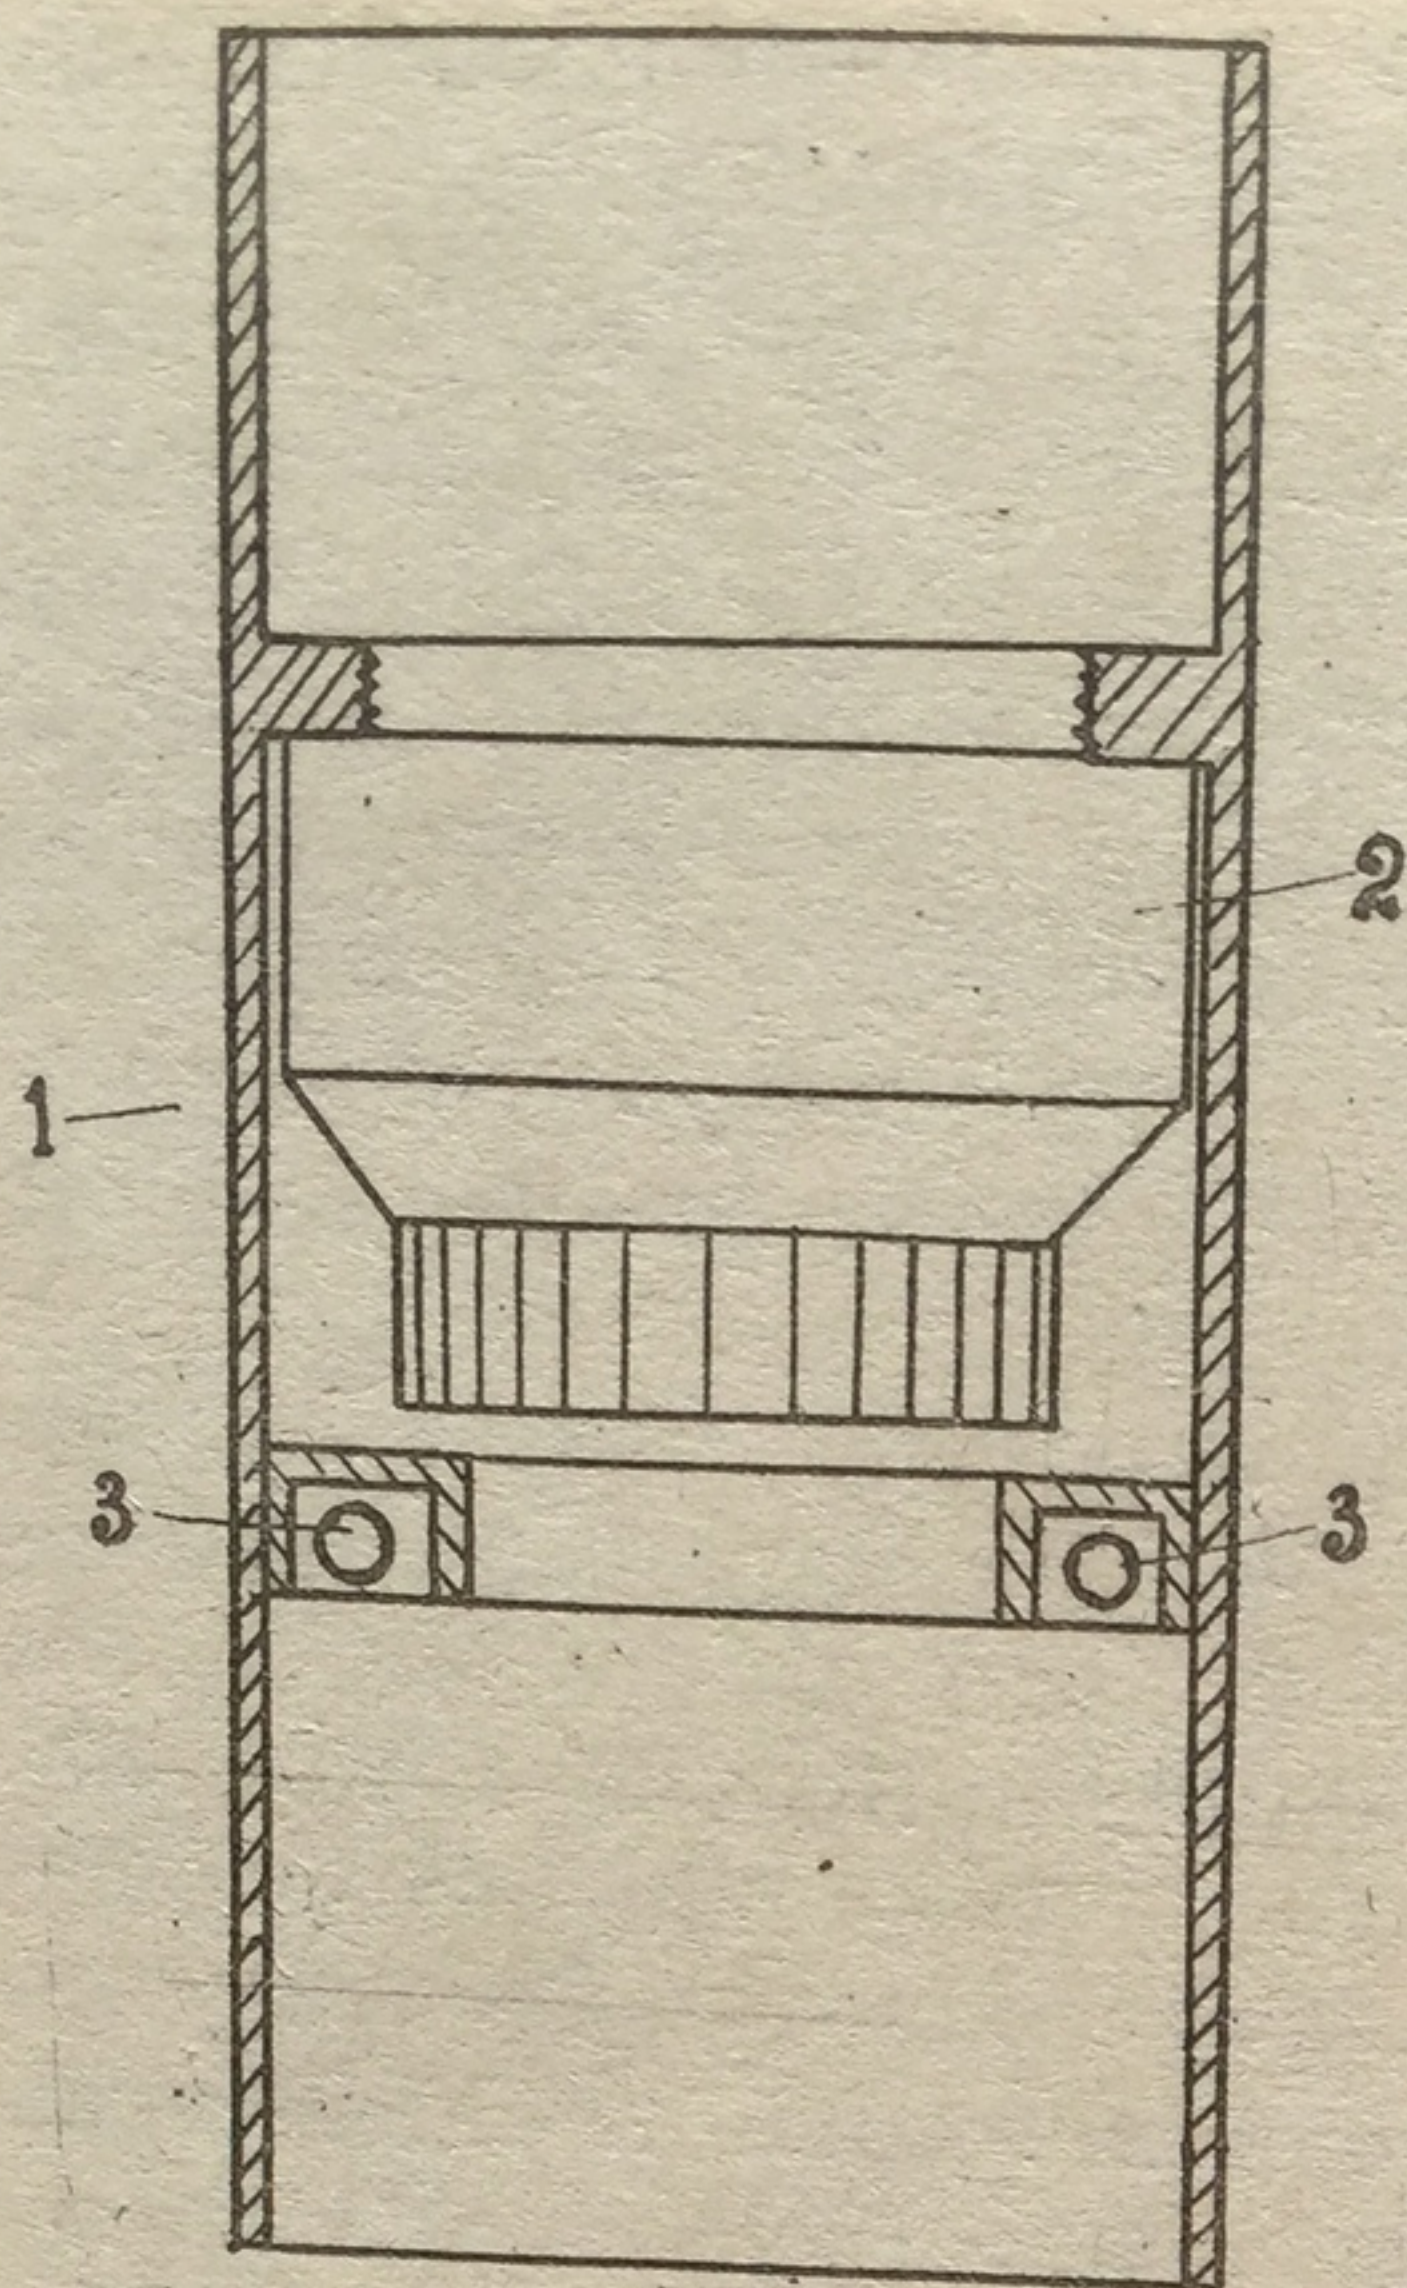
Чертеж конструкции приставки 2: 1. Корпус; 2. Объектив приставки; 3. Осветители
